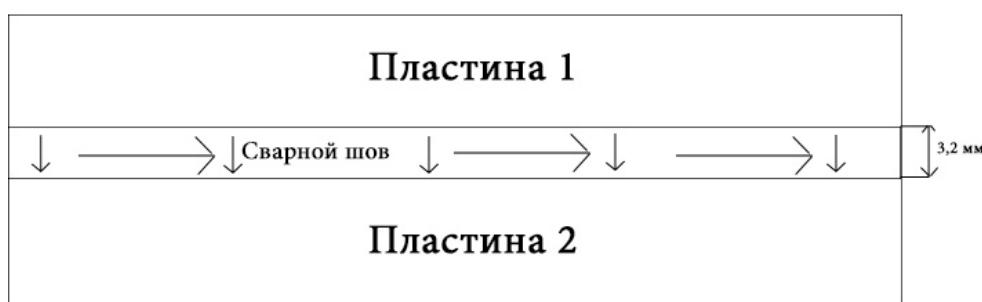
Расположение преобразователя относительно сварного шва
